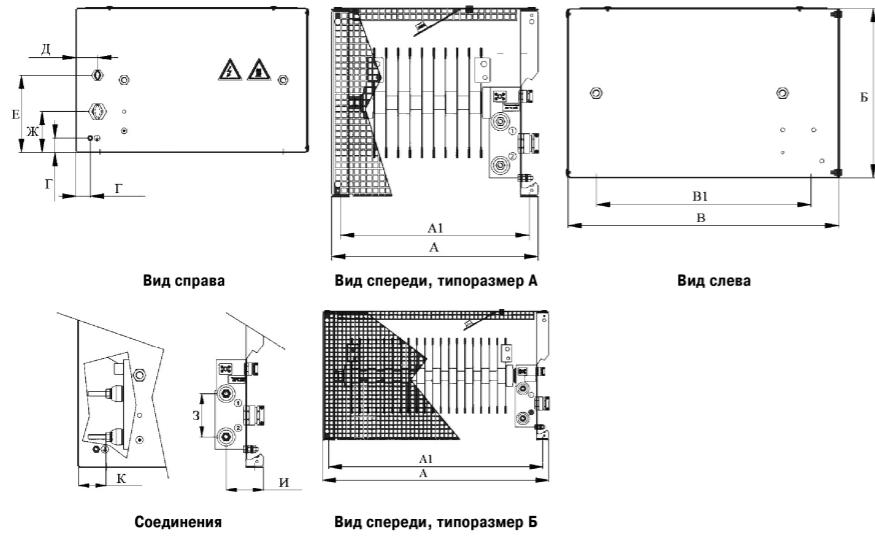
Габаритно-установочный чертеж резисторов серии РБ2
